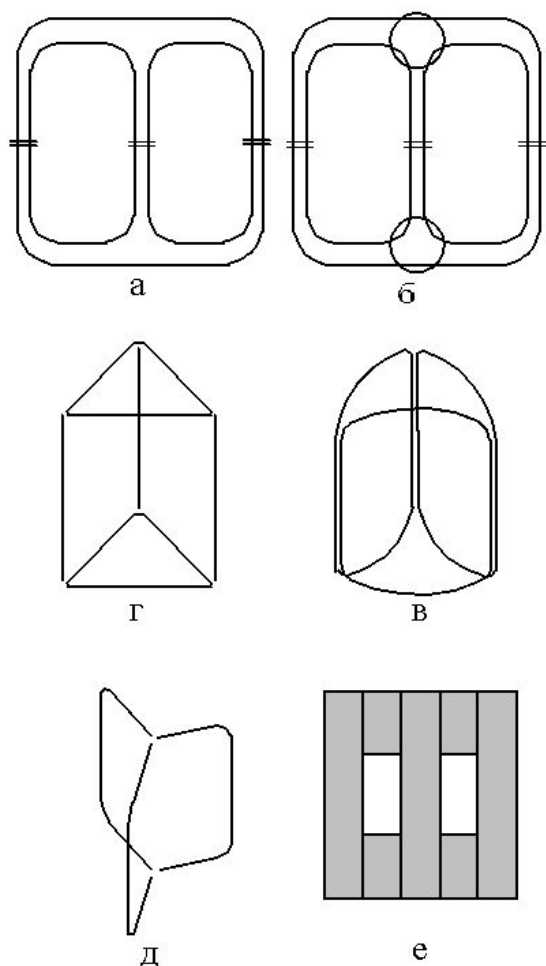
Виды конструкций магнитных систем с навитыми элементами
